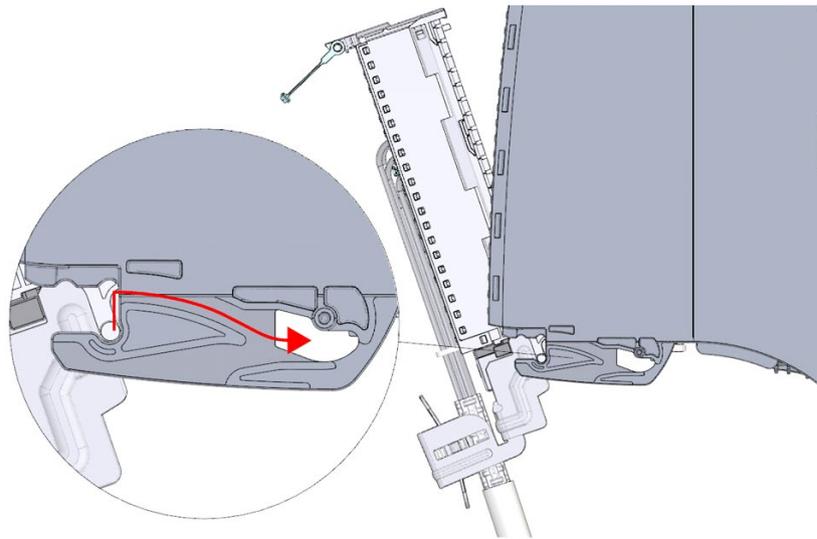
Colocar el conector frontal en la posición final desde la posición de precableado
